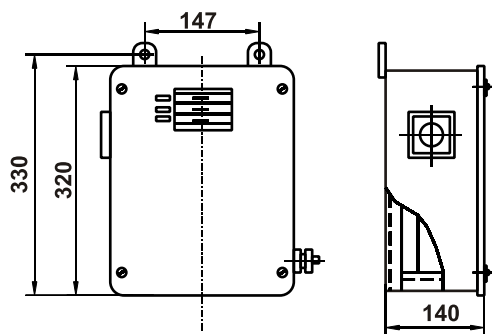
Внешний вид и габаритные размеры ЯТП-0,25
